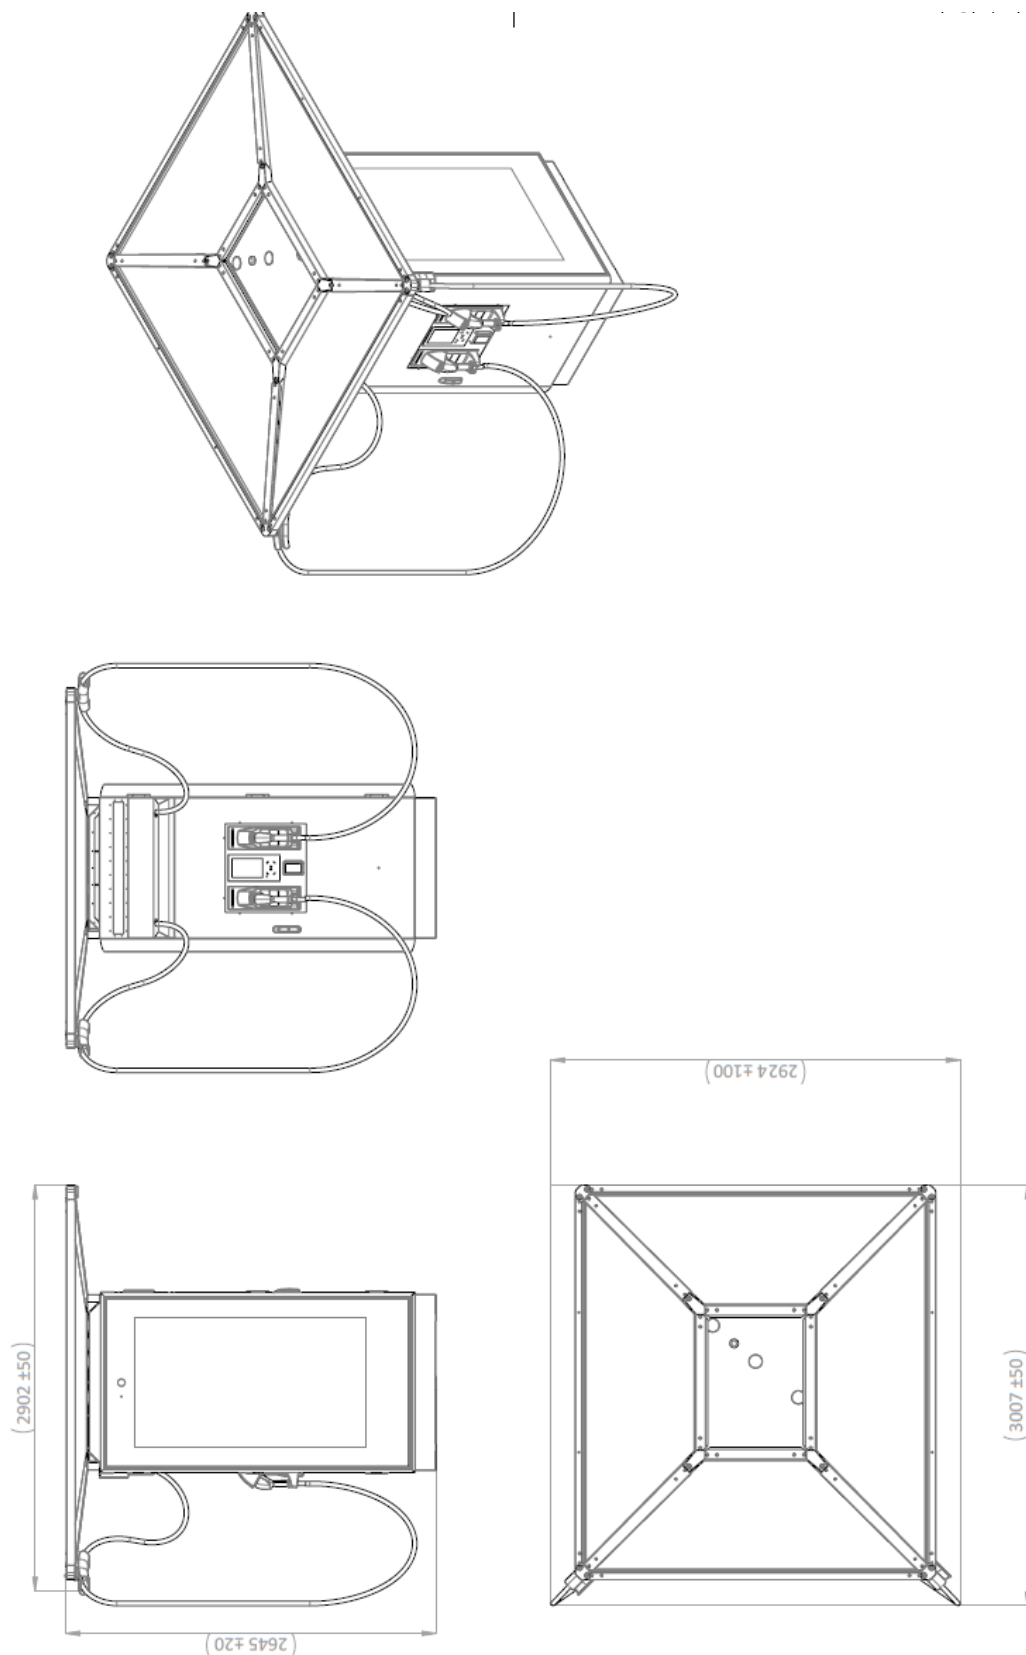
Abmessungen ChargePost mit Chargingpackage 004 Ladearme (mit Dach, Auszug aus Konstruktionszeichnung)
